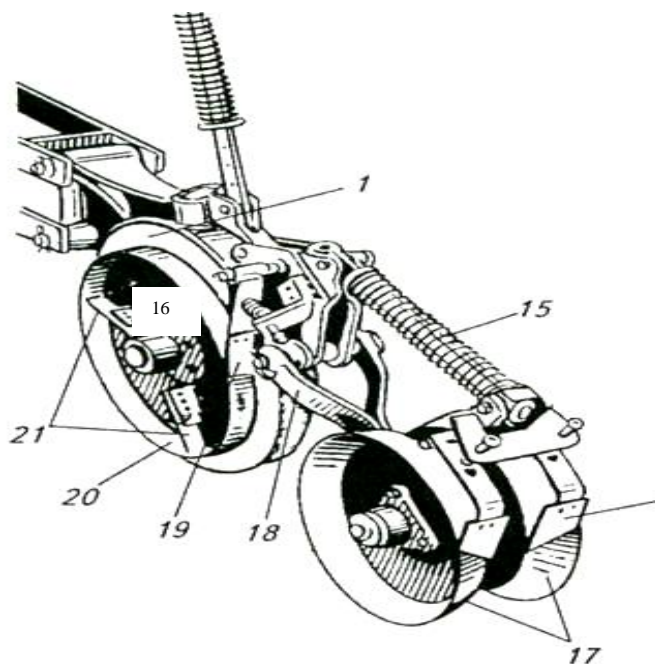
Вид двухдискового однострочного сошника с ребордам
